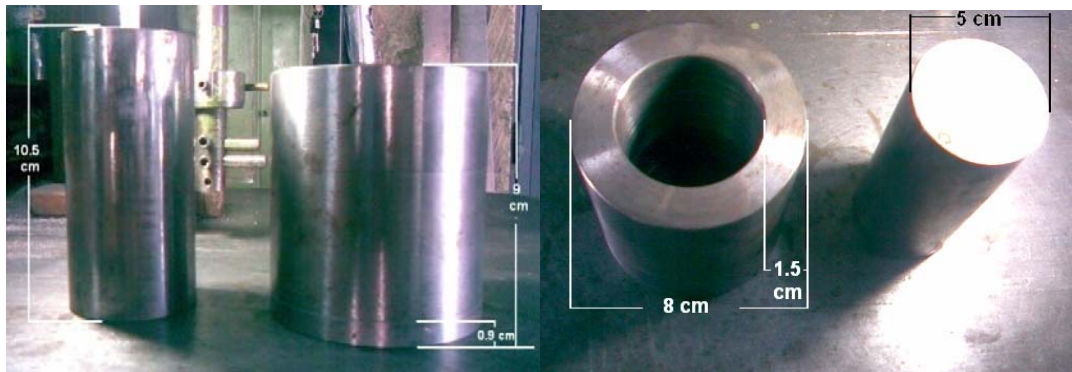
Reconstructor o pastillero utilizado para reconstruir los cortes de perforación.
